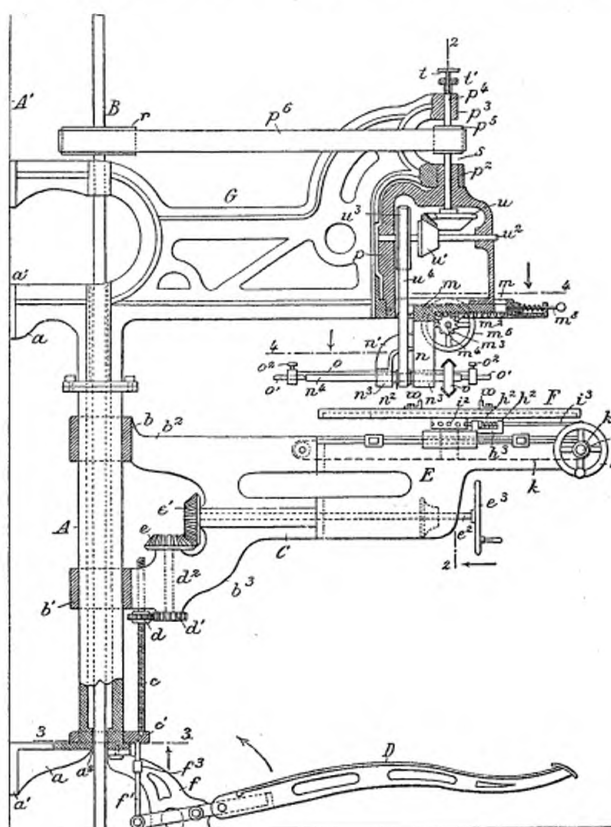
Machine Snyder à sculpter le bois. Vue de côté.
